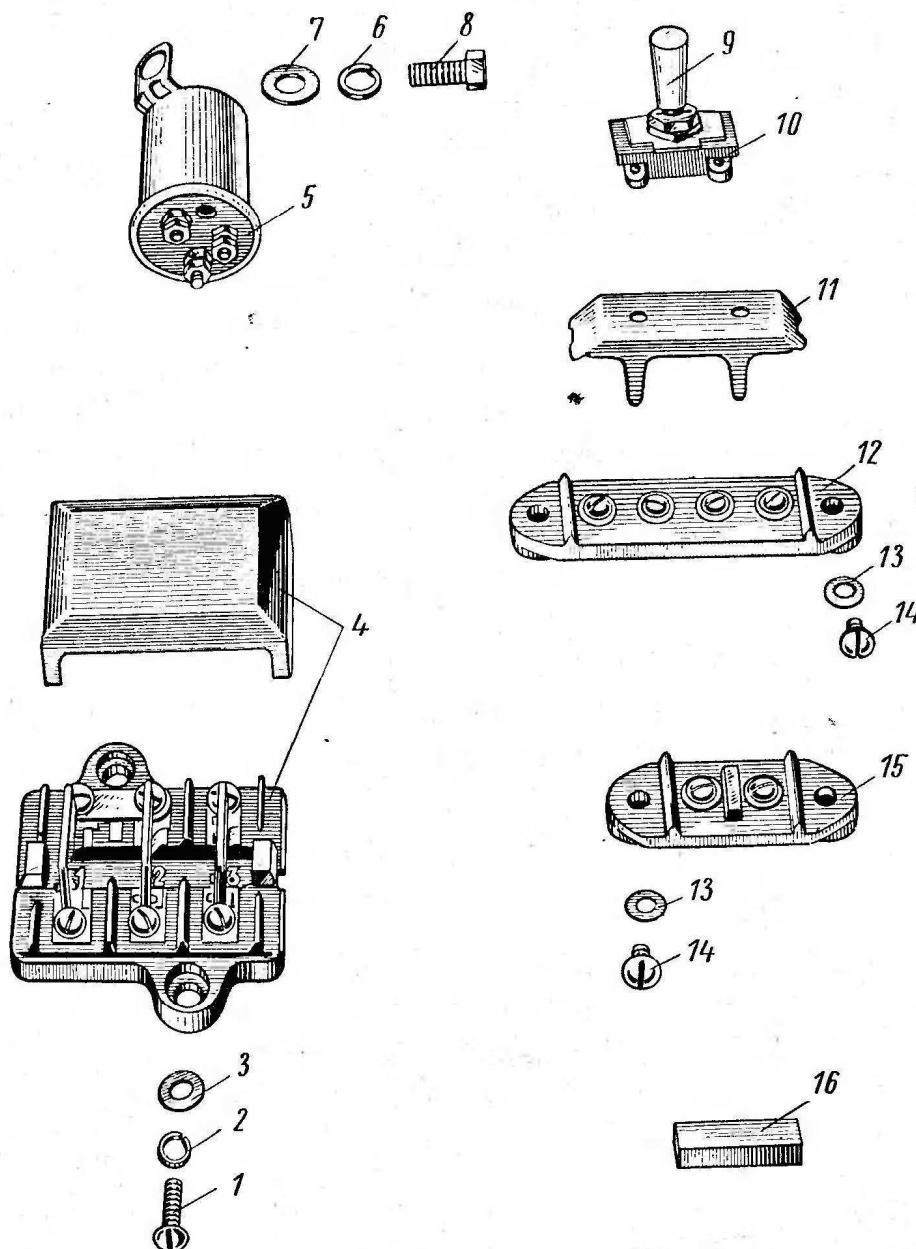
Sicherungskasten, Winkelunterbrecher mit Umschalter und Leitungsanschluß
